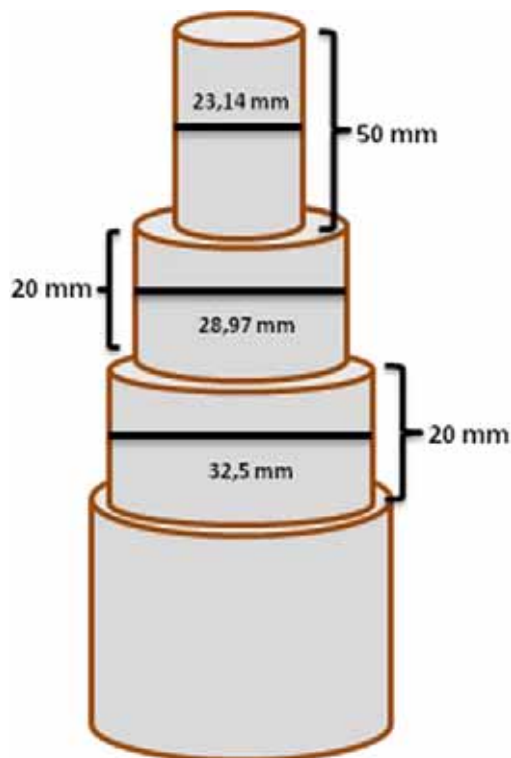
Dimensões dos corpos de prova após as 3 usinagens.
